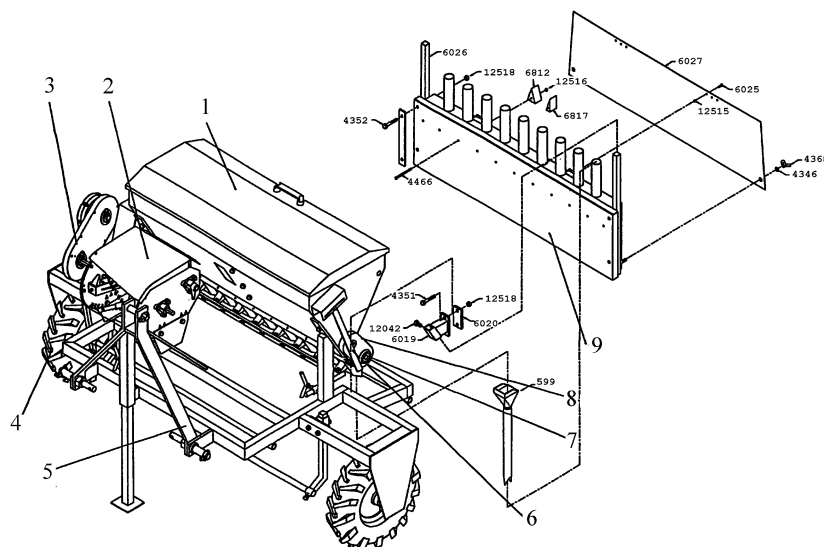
Общий вид сеялки «Egedal»: 1 – бункер для семян; 2 – многоступенчатый редуктор с 20 передачами; 3 – цепная передача; 4 – правое приводное колесо; 5 – рама с навеской; 6 – рычаг регулировки размера щели высевающего аппарата; 7 – вал высевающих аппаратов; 8 – цепная передача привода ворошилки семян; 9 – приставка для сплошного посева семян
